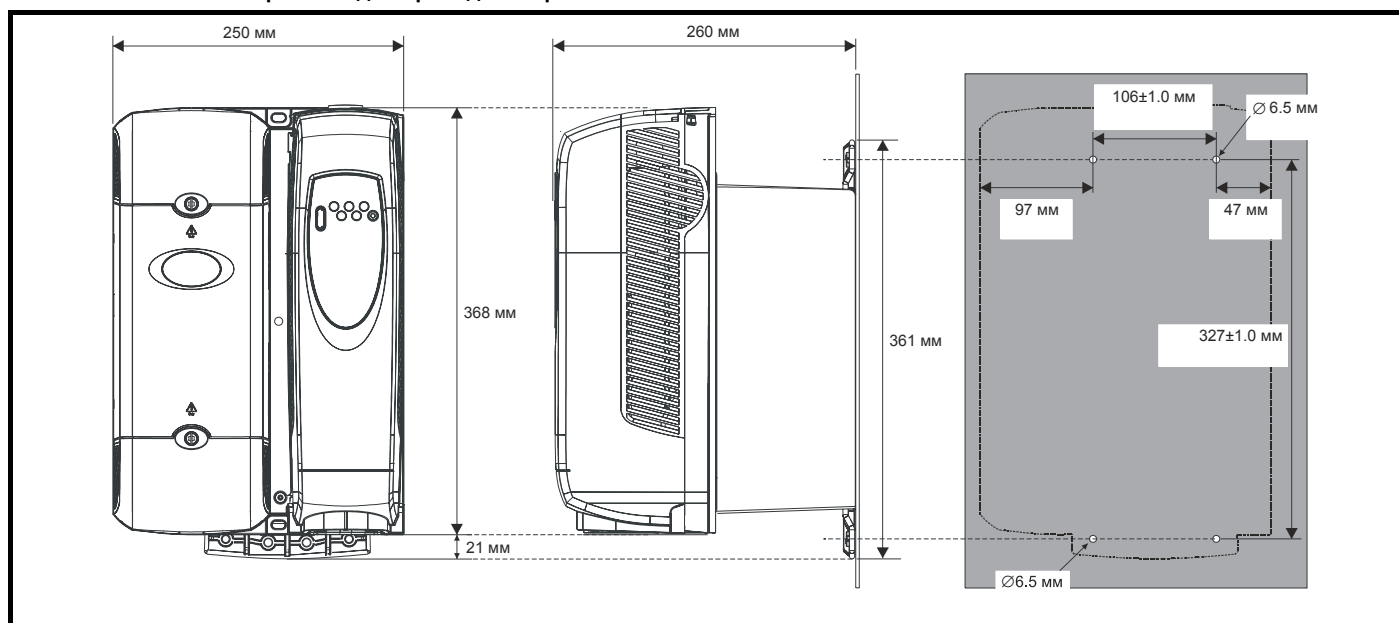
Монтаж к поверхности для привода габарита 4
